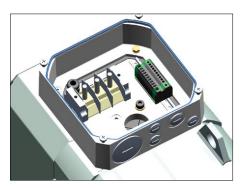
Plaque à bornes pour tailles de moteur 100 - 132
